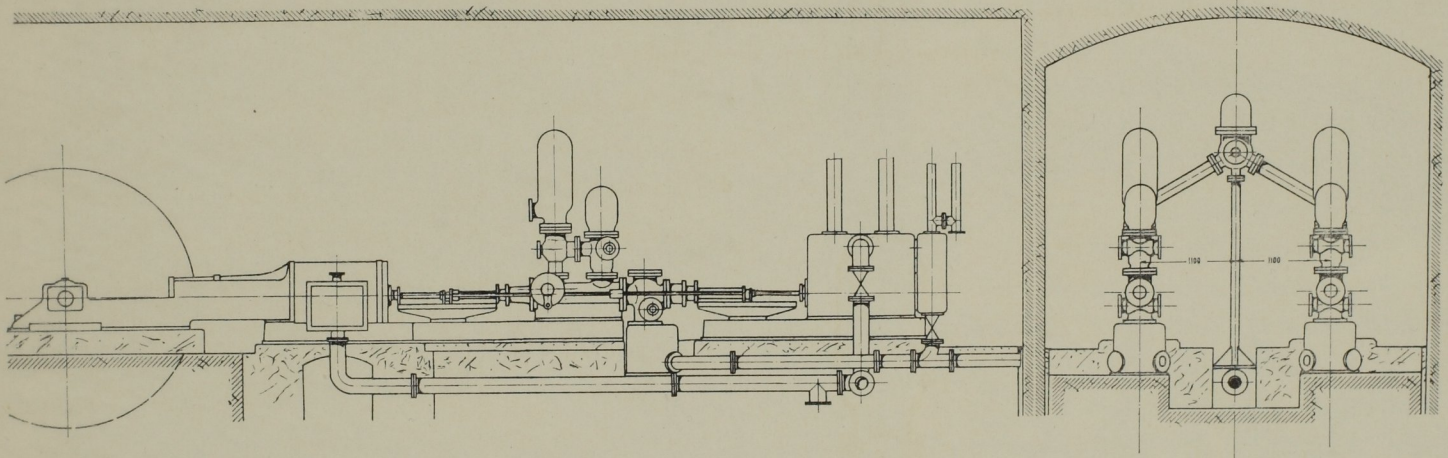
Seitenansicht und Querschnitt der Maschine. Masst. 1:80.
